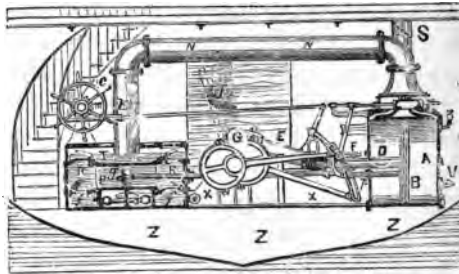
Machine marine à hélice horizontale à connexion directe.
